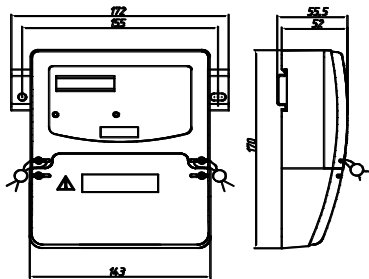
Загальний вигляд лічильника ЦЕ6804-У у корпусі Р32
